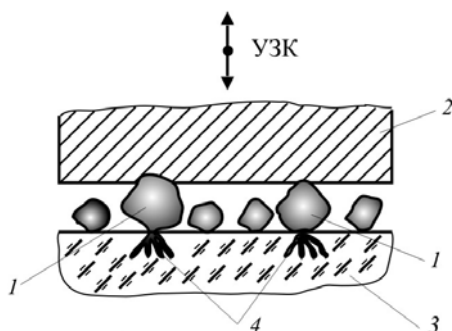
Схема взаимодействия абразивных зерен с поверхностью заготовки и инструмента в процессе ультразвуковой размерной обработки: 1 – абразивные зерна; 2 – инструмент; 3 – обрабатываемый материал; 4 – микротрещины
